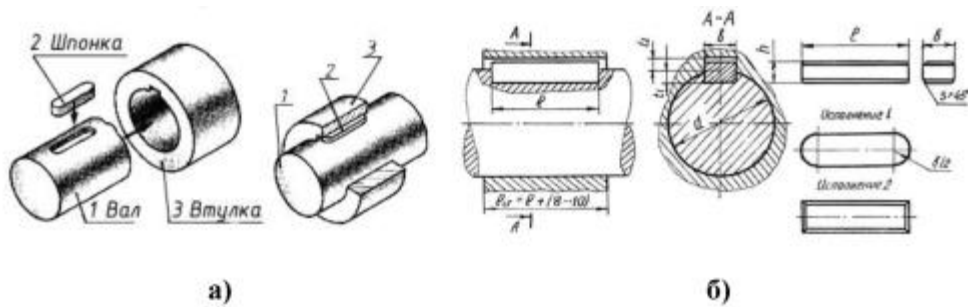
Шпоночное соединение (а), чертеж шпоночного соединения и шпонки (б)
